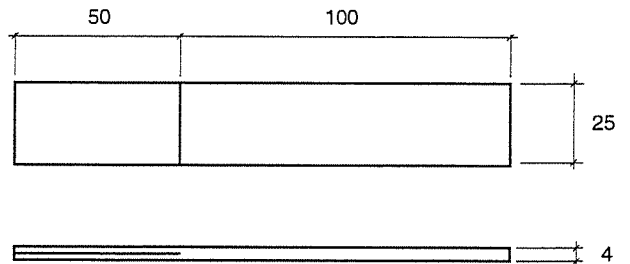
Dimensiones de la probeta ENF elegida. probeta ENF.
